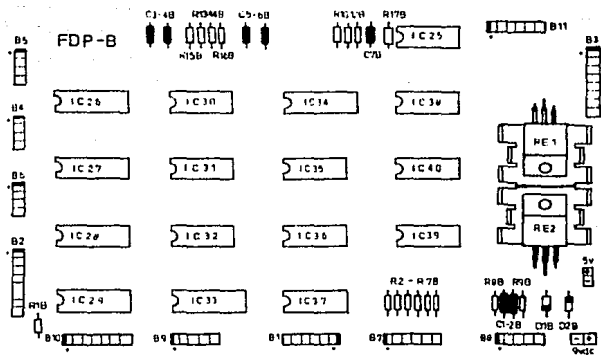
Ensamble de componentes tarjeta FDP-B.
